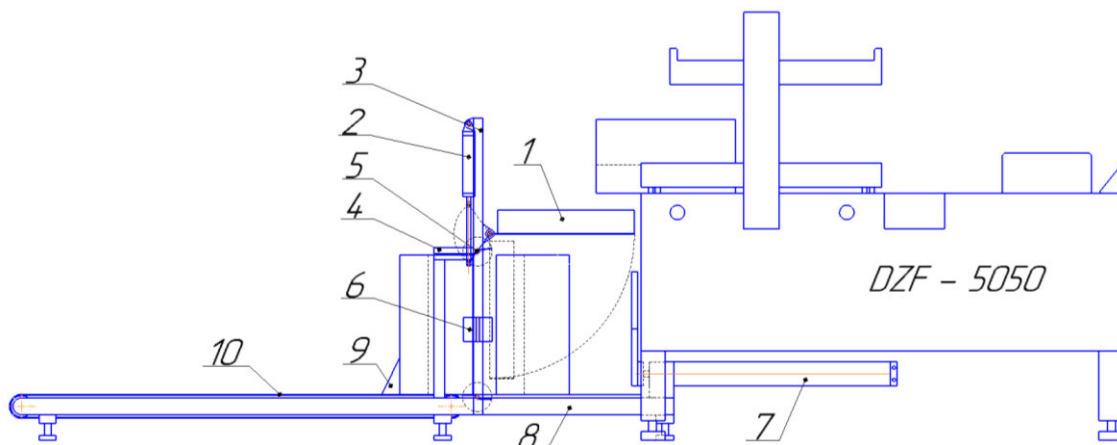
DZF-5050 Полуавтомат для складывания и заклейки дна коробов
